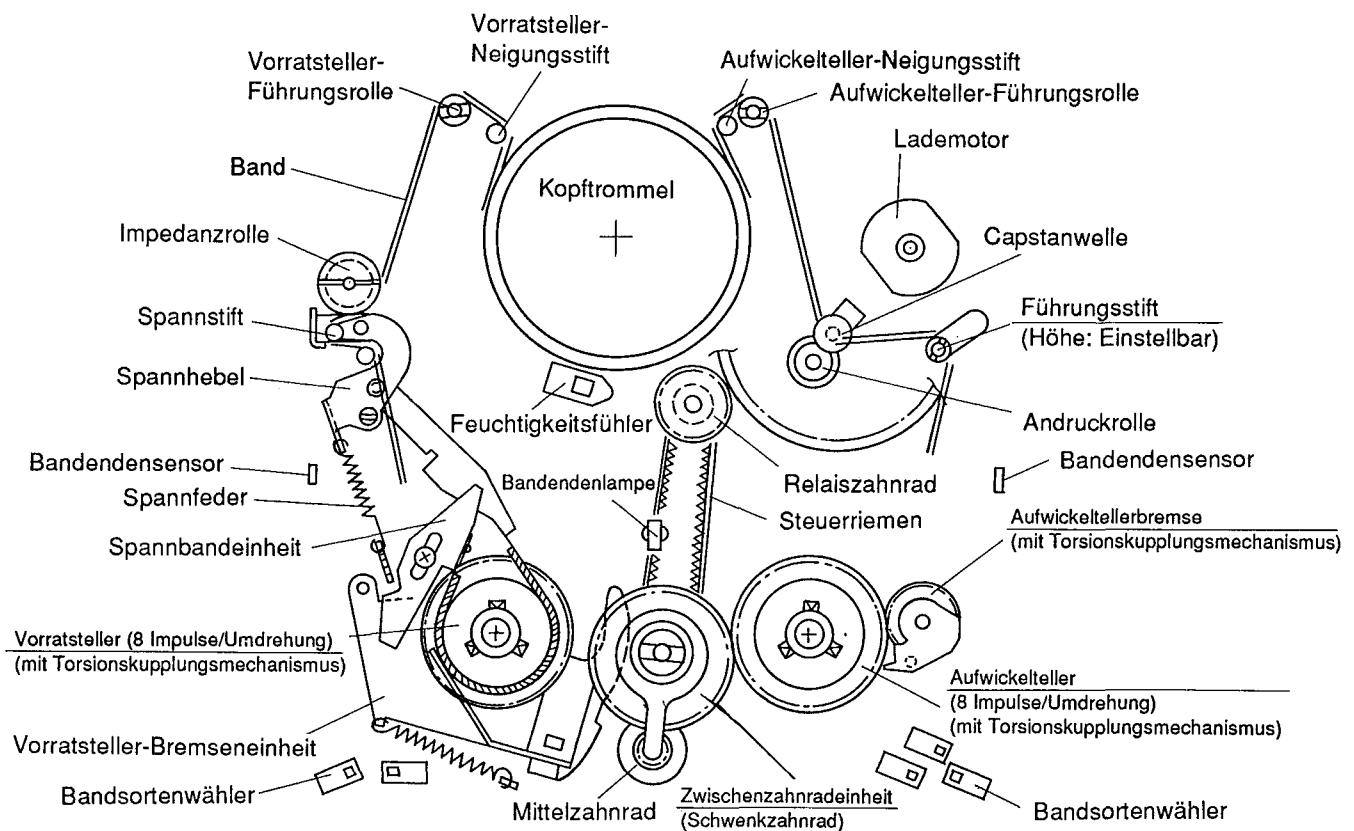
Anordnung der wichtigsten Komponenten in dem TH-Chassis (Draufsicht)
